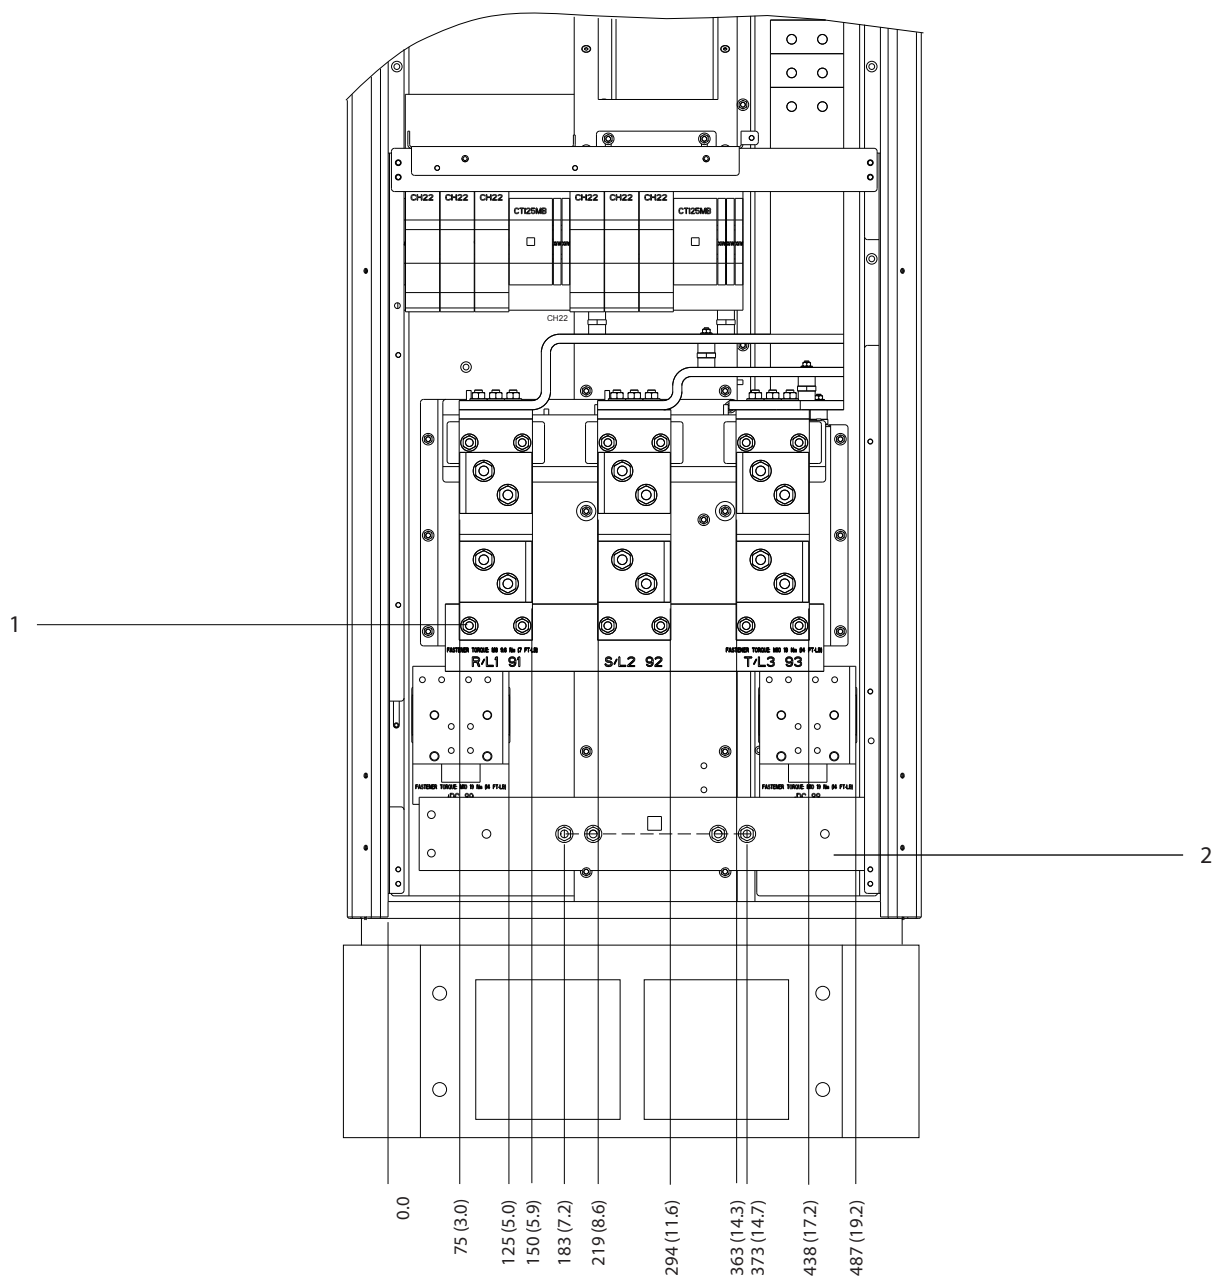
Размеры клемм для шкафа дополнительных устройств F3–F4 с автоматическим выключателем/выключателем в литом корпусе, вид спереди
